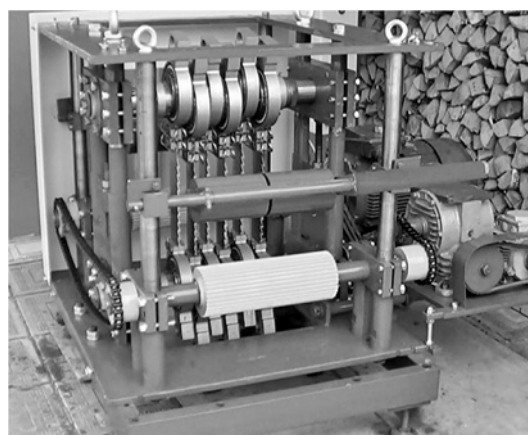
Опытный образец многопильного станка М2002 для распиловки двухканатного бруса (без кожуха)
